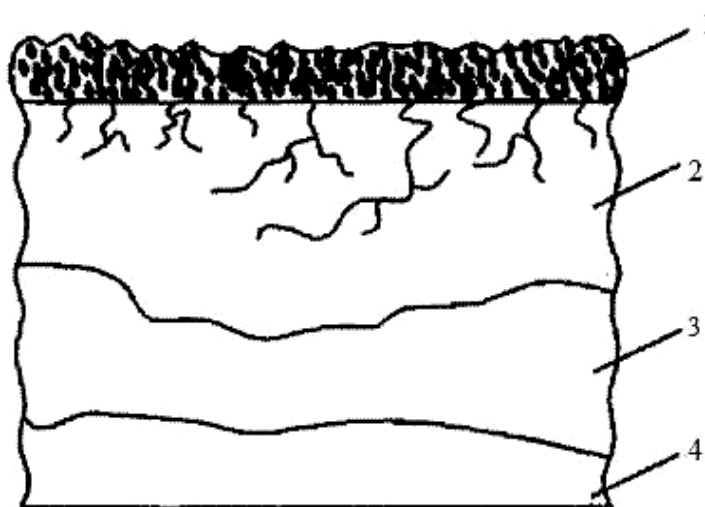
Структура порушеного при механічній обробці поверхневого шару.
